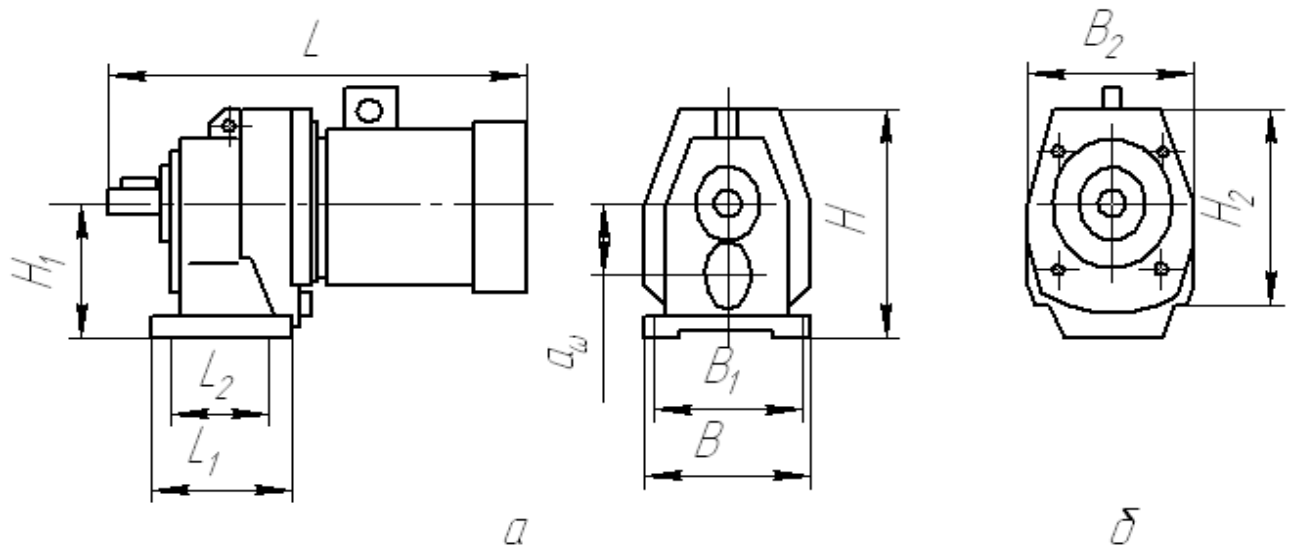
Габаритні і приєднувальні розміри асинхронного циліндричного двохосьового мотор-редуктора:
